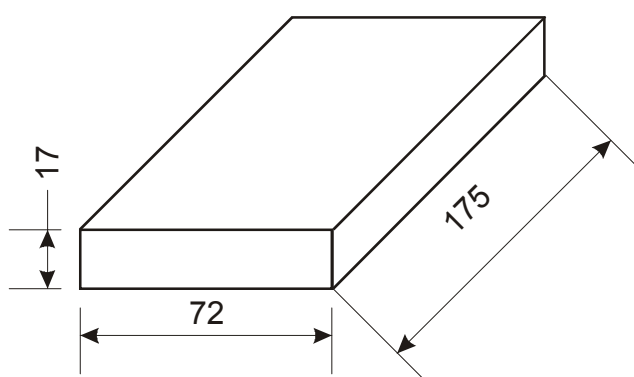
Габаритный чертеж мезонинного модуля FXS
